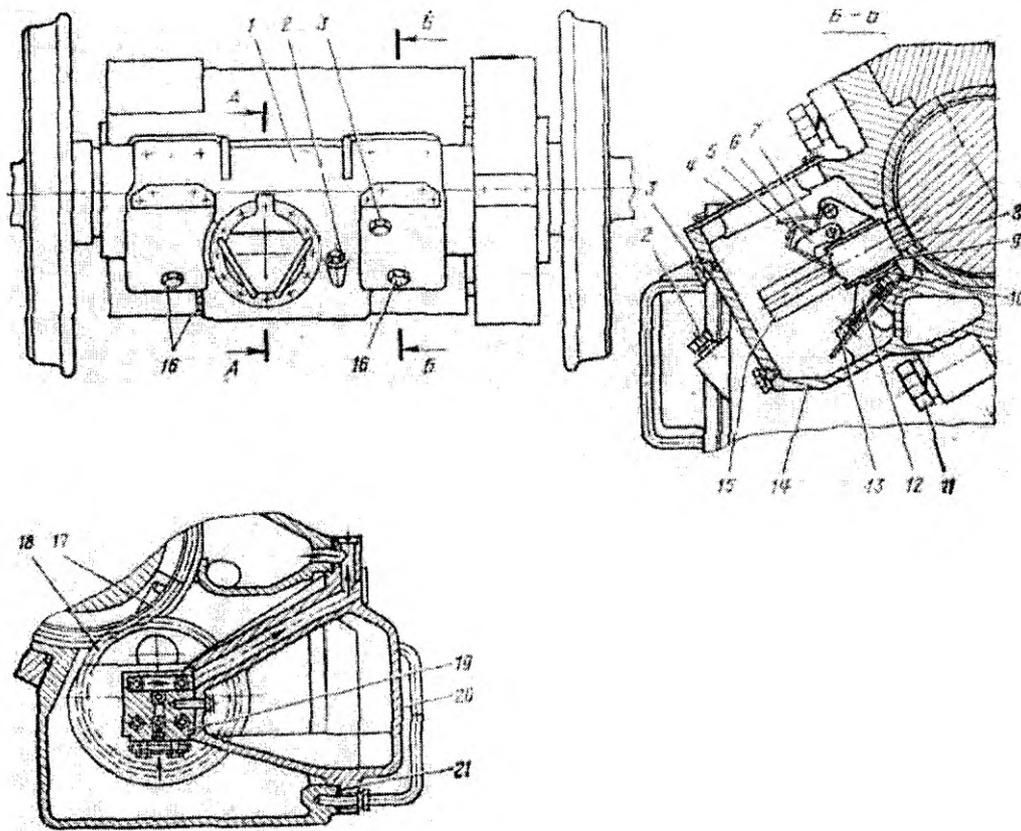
Моторно-осевые подшипники с циркуляционной системой смазки: 1 - единый осевой подшипник; 2 - пробка заправочной горловины; 3 - пробка для контроля уровня смазки; 4, 20 - крышки; 5 - пружина; 6 - рычаг; 7-фиксатор; 8-коробка; 9 -пружина пластинчатая; 10 - направляющая корпуса; П. 13- болты; 12 - корпус польстера; 14 - корпус подшипника; 15 - пакет фитилей; 16 - пробки сливные; 17, 18 - шестерни; 19 -насос шестеренный; 21 - прокладка
